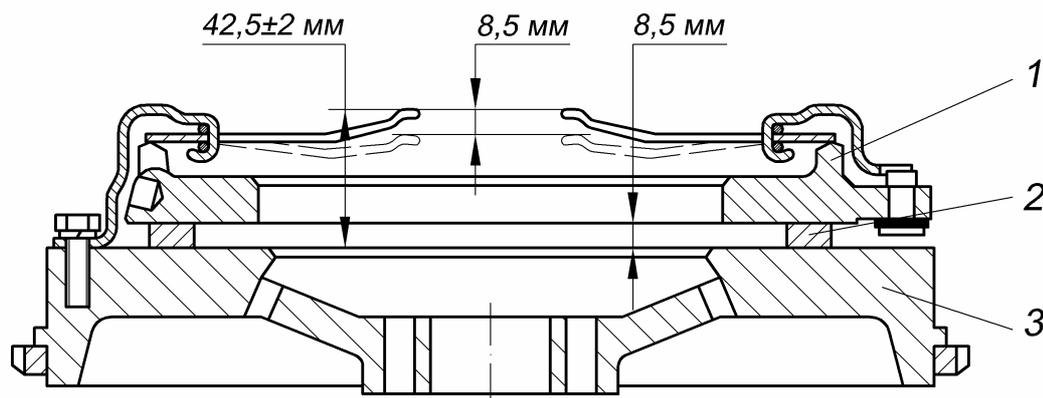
Регулировка концов лепестков и проверка нажимного диска сцепления:
